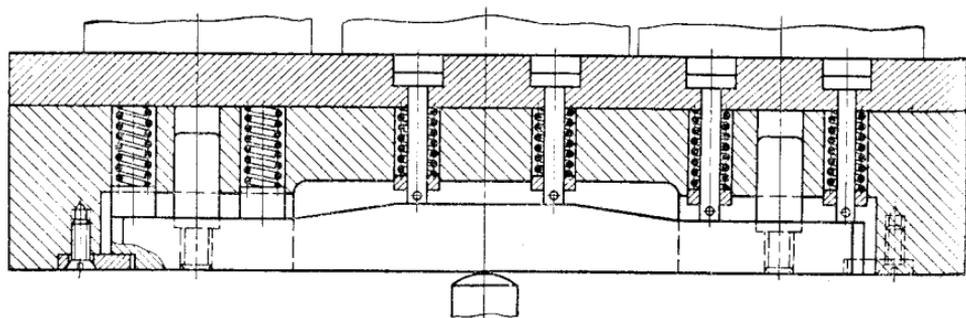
Безрычажный механизм для нескольких выталкивателей, расположенных на одной оси
